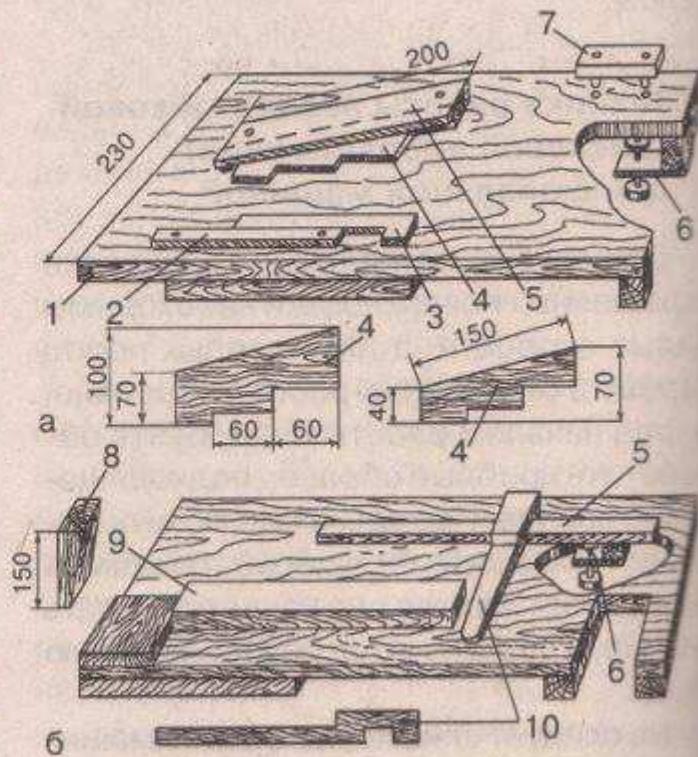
Съемные крышки столярного верстака: а — супором; б — с ползуном; 1 — основание; 2 — боковая рейка; 3 — вкладыш; 4 — упор для строгания; 5 — направляющая; 6 — струбцина; 7 — упор для пиления; 8 — клин; 9 — заготовка; 10 — ползун
